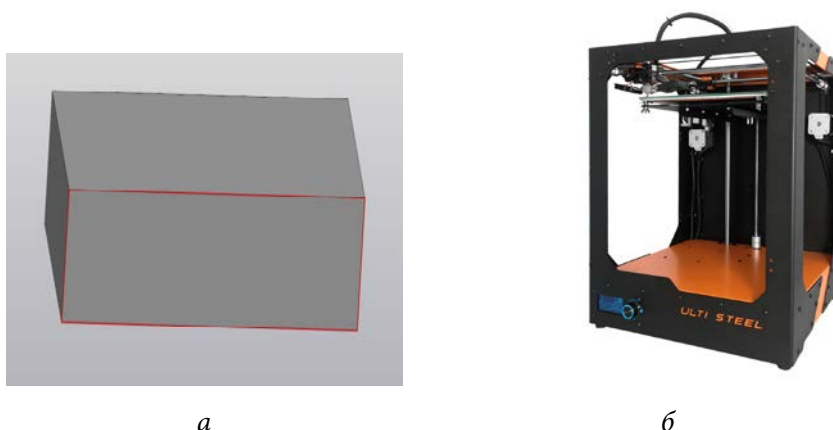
Модель образца (а) и 3D-принтер для их печати (б)
